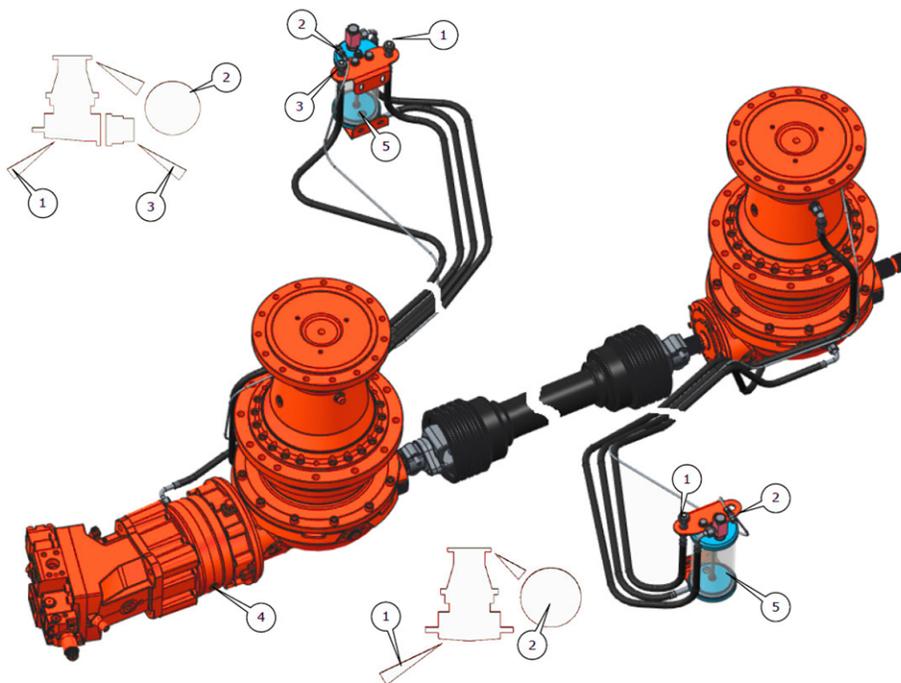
Contrôle du niveau d'huile et graissage du boîtier planétaire
